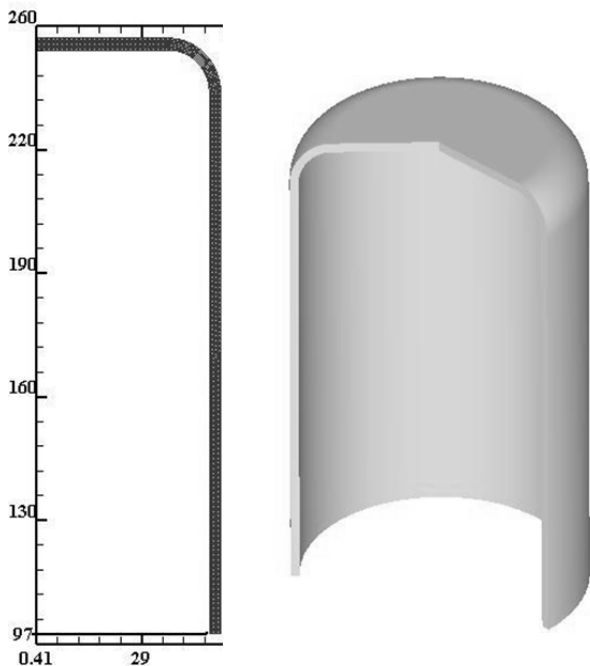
Розміри половини вихідної заготовки (мм) та загальний вигляд в розрізі
